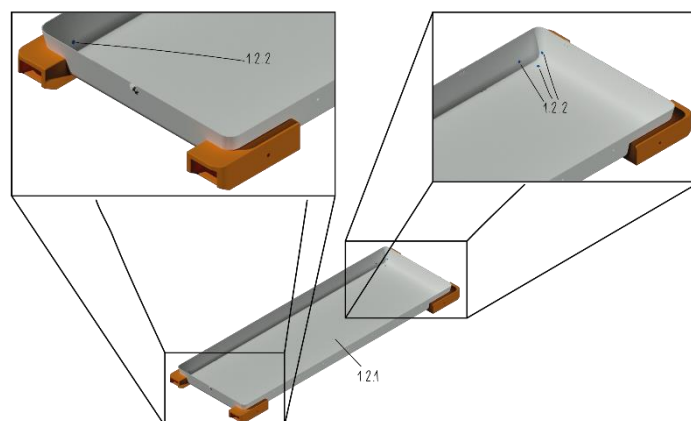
Ensamblaje subconjunto 1.2 (parte b) (2)
